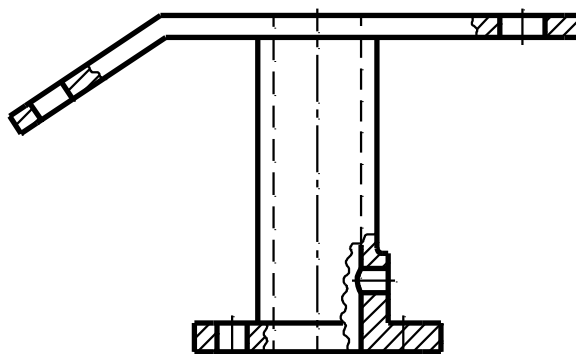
Главный вид с местными разрезами, выполненными для выявления отверстий в детали
